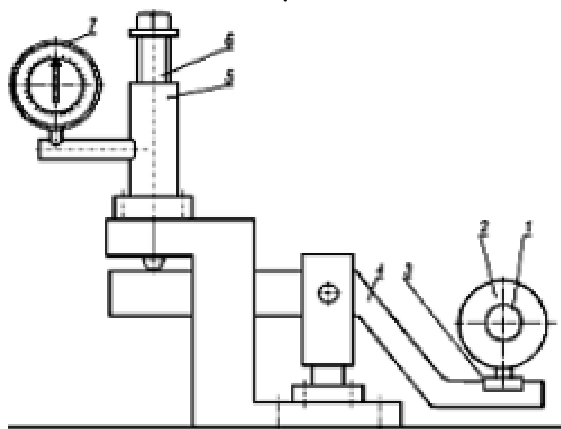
Нагружающее устройство испытательной машины трения МИ-1М: 1 – вал машины; 2 – вращающийся ролик; 3 – неподвижный образец; 4 – рычаг; 5 – корпус с гидрокамерой; 6 – винт; 7 – манометр
